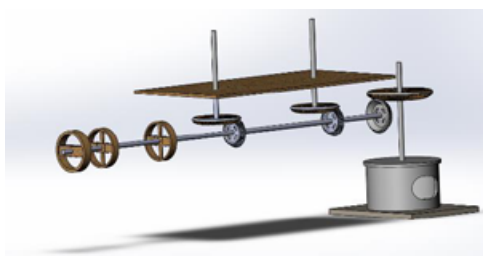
SolidWorks de la planta inferior. Vista des de les politges.
